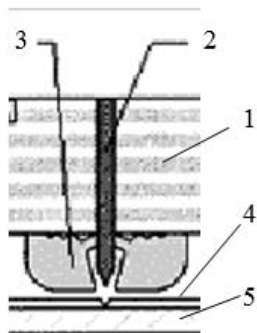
Устройство штанцевальной формы для вырубki заготовок матриц при помощи типографского пресса. 1 – основание штанцформы, 2 – режущая линейка (нож), 3 – эжектор, 4 – раскраиваемый материал, 5 – рабочий стол.
